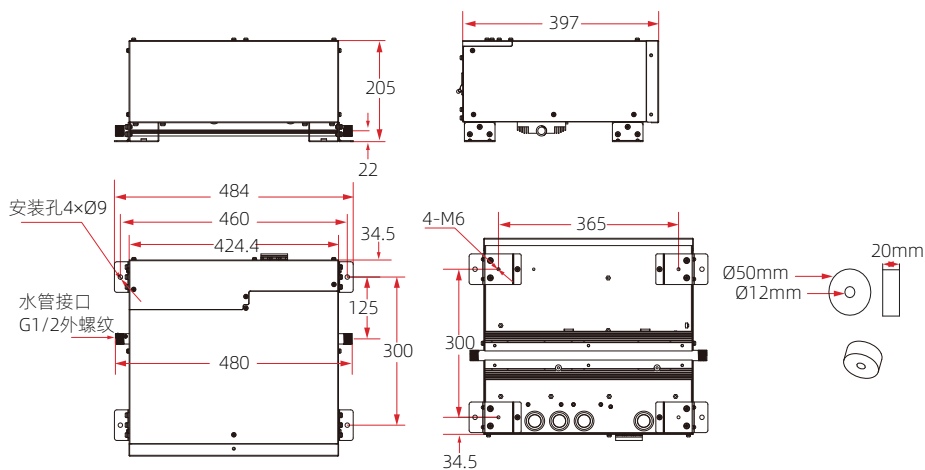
（分体液冷 - 侧出冷却管）外型尺寸安装尺寸及减震垫示意图 (AWD100-4T0501~AWD100-4T1804) (单位: mm)
